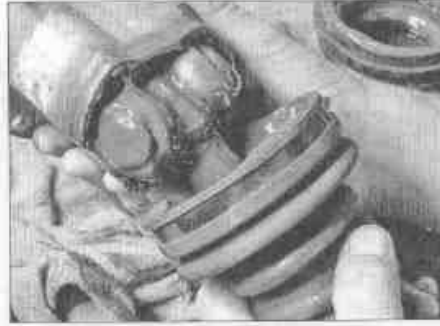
Снимите чехол с внутреннего ШРУСа и сдвиньте корпус шарнира с трипода
